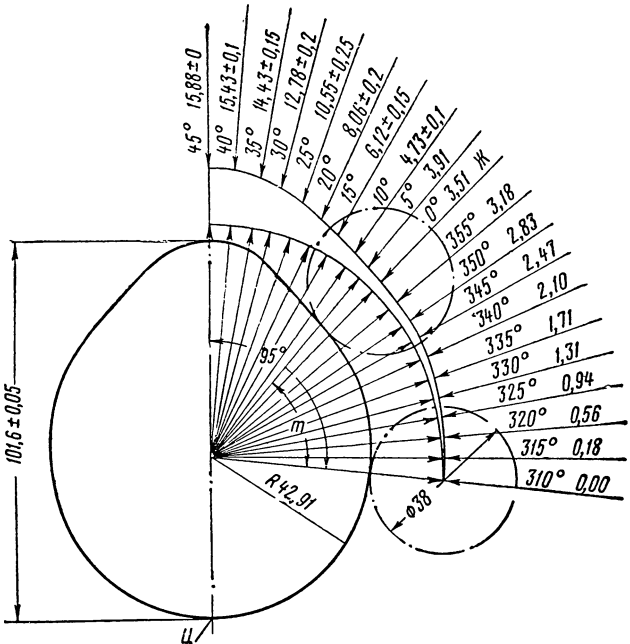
Профиль кулачка кулачкового вала топливных насосов
